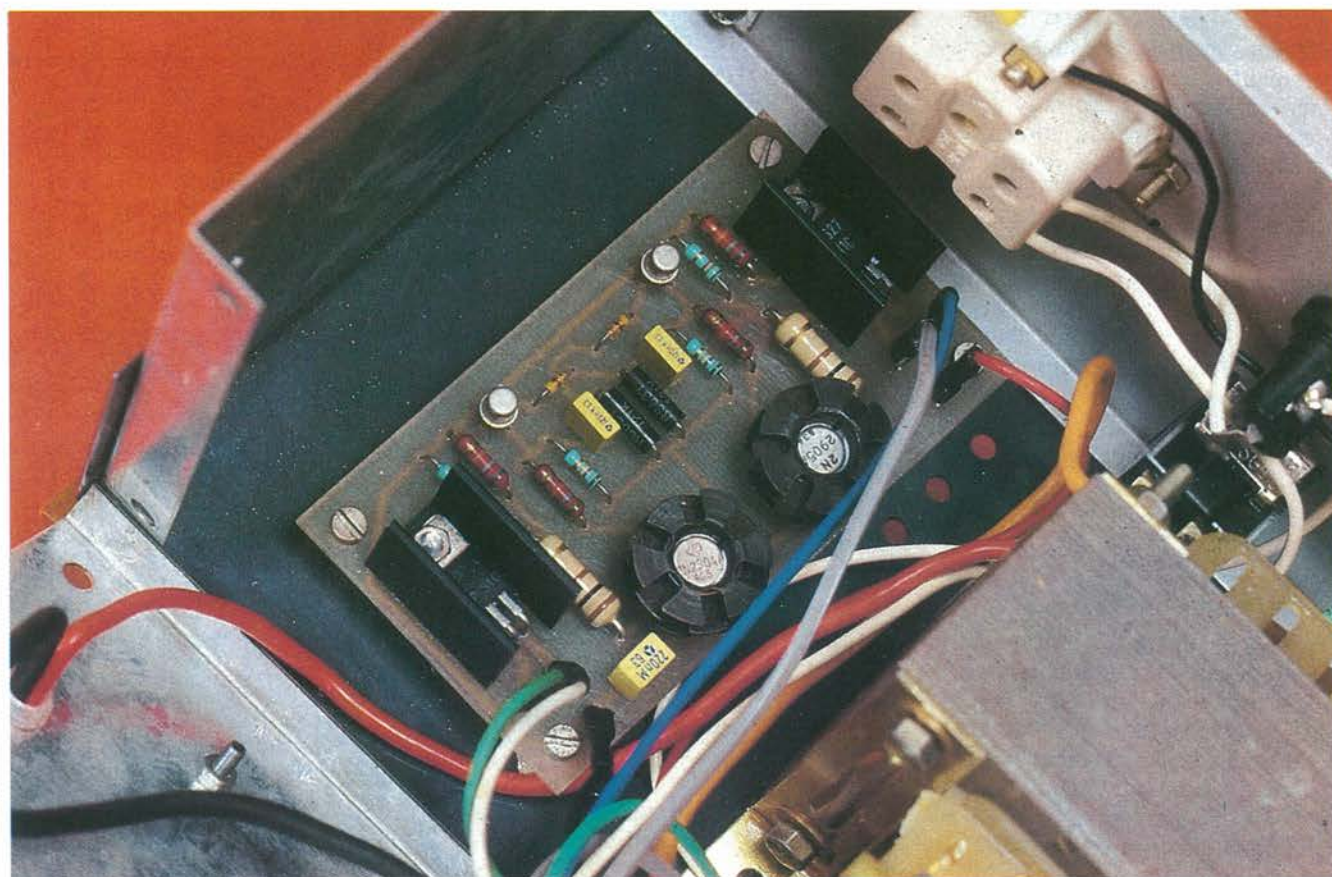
Fissaggio del circuito stampato sul fondo del mobiletto.
